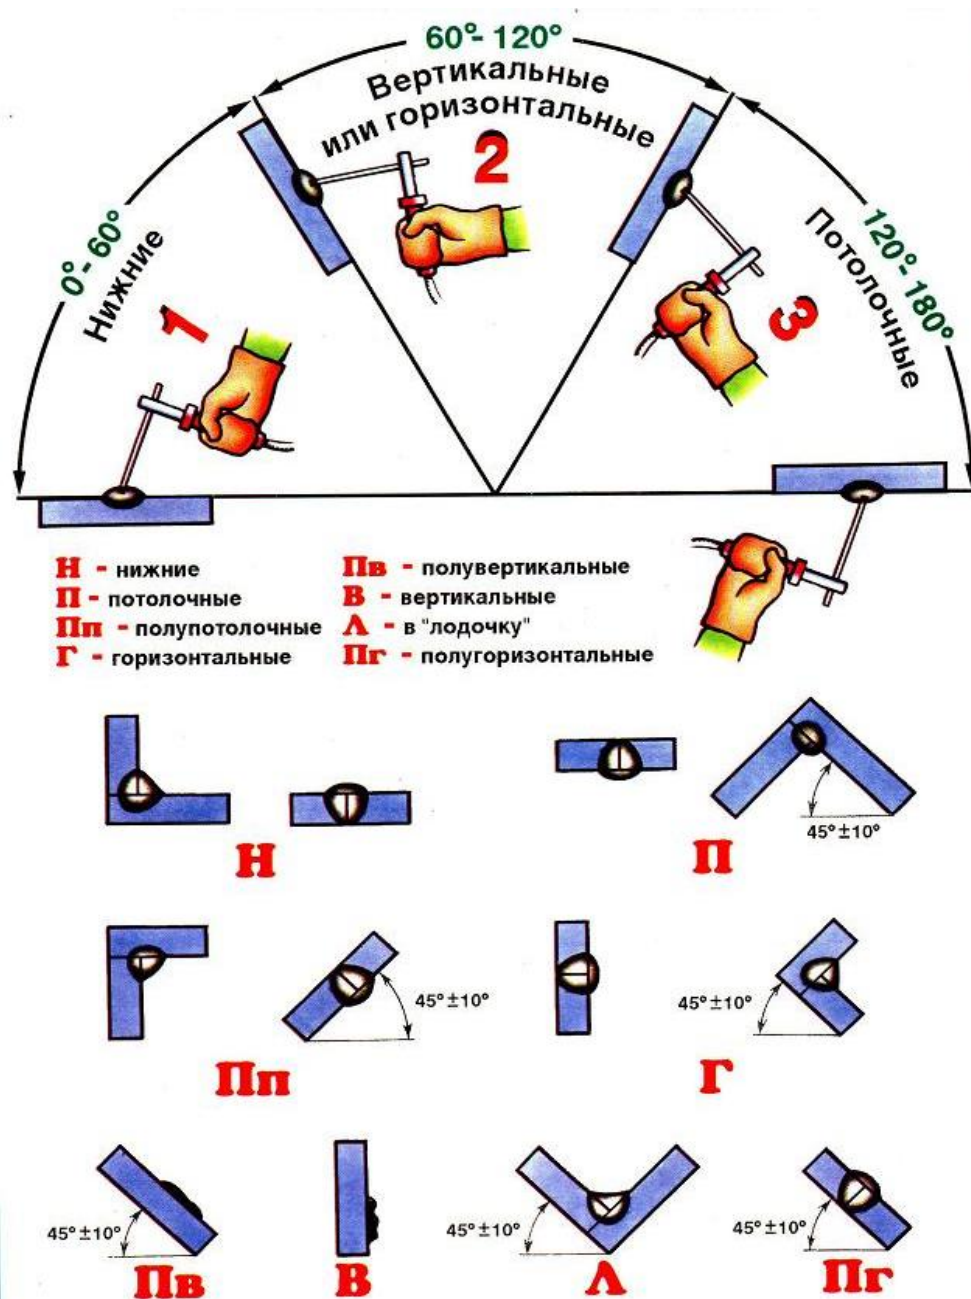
Возможные пространственные положения при ручной дуговой сварке
